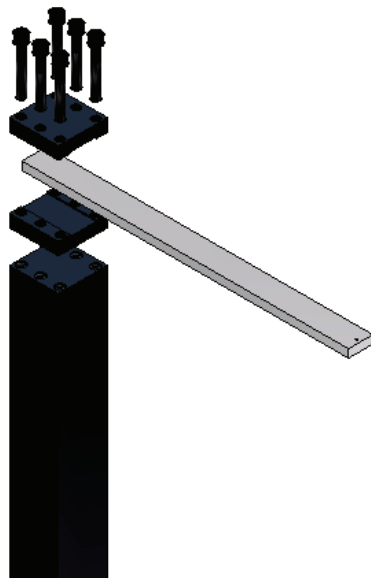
Detalle de ensamble de viga y soporte de viga tipo prensa.
